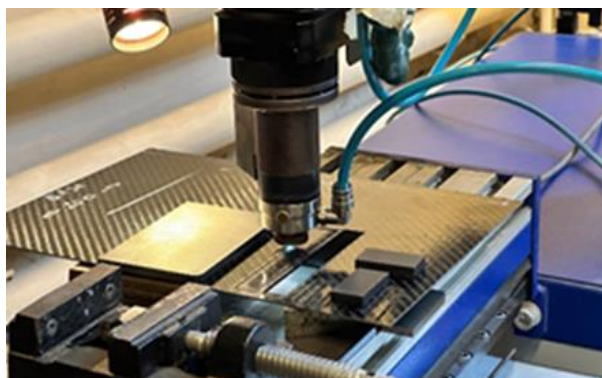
Процесс изготовления образцов ПКМ методом лазерной резки
